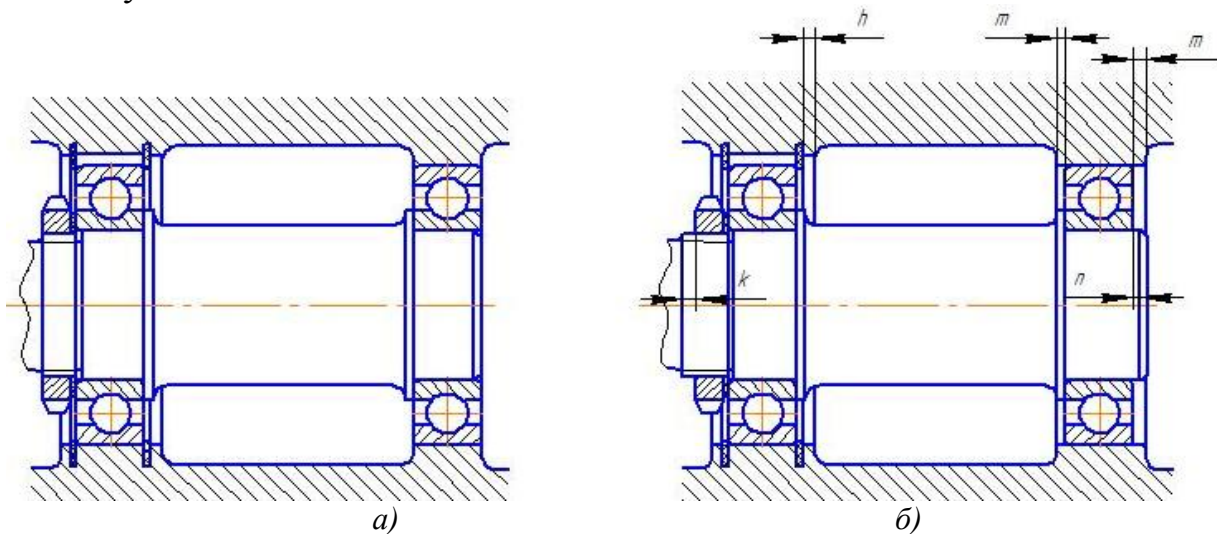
Вал, який встановлений в посадочній поверхні корпусу на підшипниках кочення:
